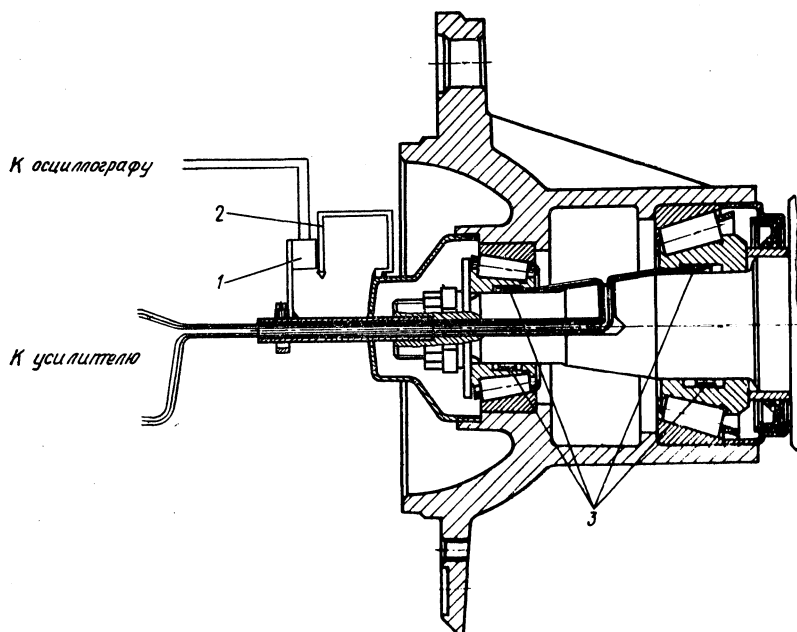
Схема расположения тензодатчиков на подшипниках ступицы колеса:
